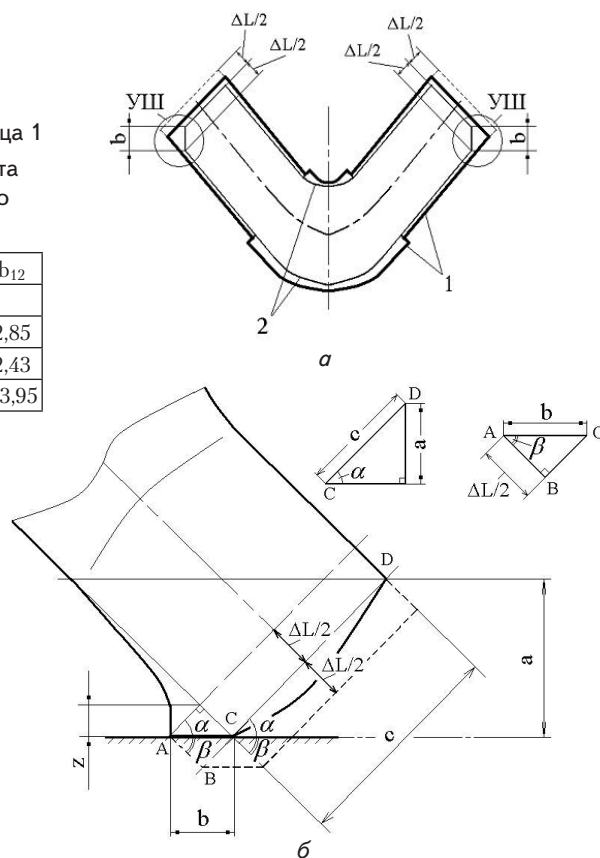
К учету искажения торцов заготовки, профилированной продольным изгибом, при дальнейшей штамповке: а – размещение поковки в гравюре штампа; б – схема к расчету увеличения длины развертки профилированной заготовки; 1 – контуры ручья; 2 – контуры заготовки
